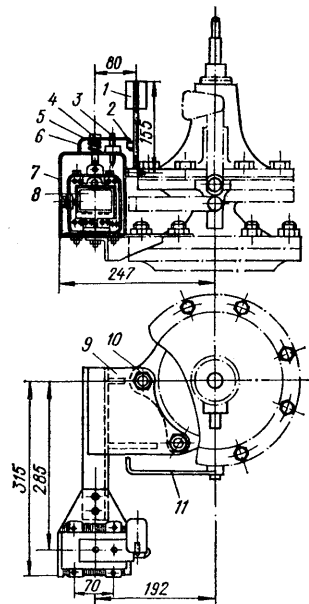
Клапан ПКН (ПКВ) с электромагнитной приставкой. 1 — молоточек; 2 — штифт; 3 — направляющий штырь; 4 — шток; 5 — пружина; 6 — скоба; 7 — рамка; 8 — электромагнит; 9 — кронштейн; 10 — крепежные болты; 11 — плечо анкерного рычага.
